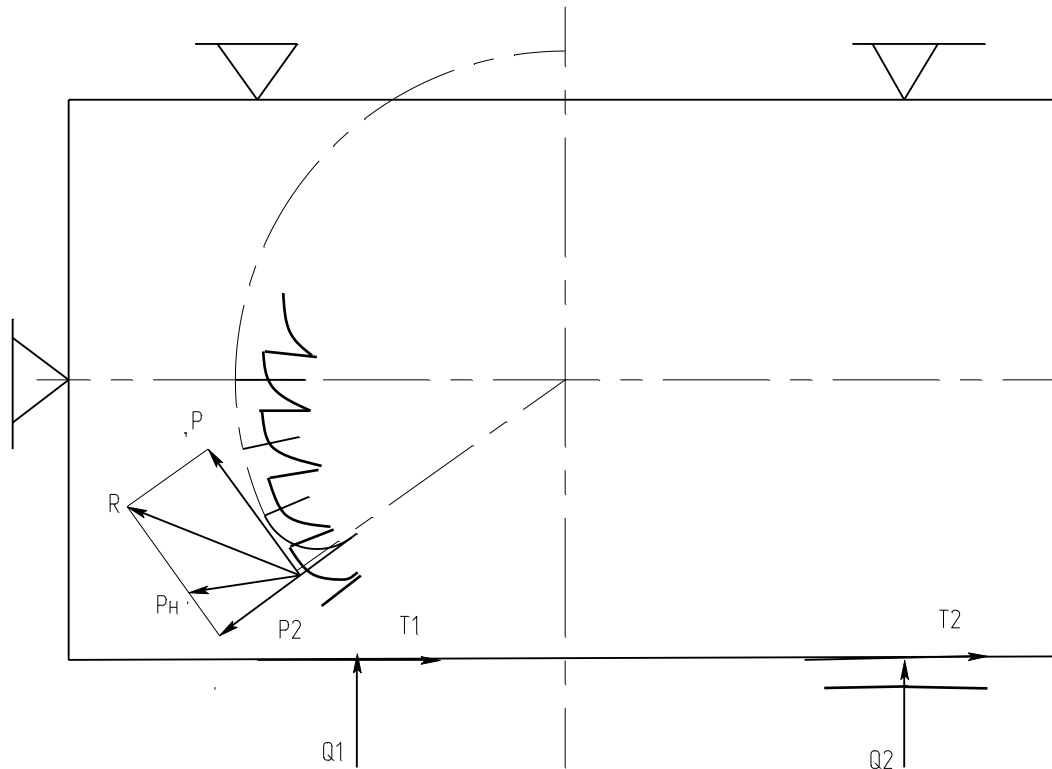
Зусилля затиску фрезерного пристрою
